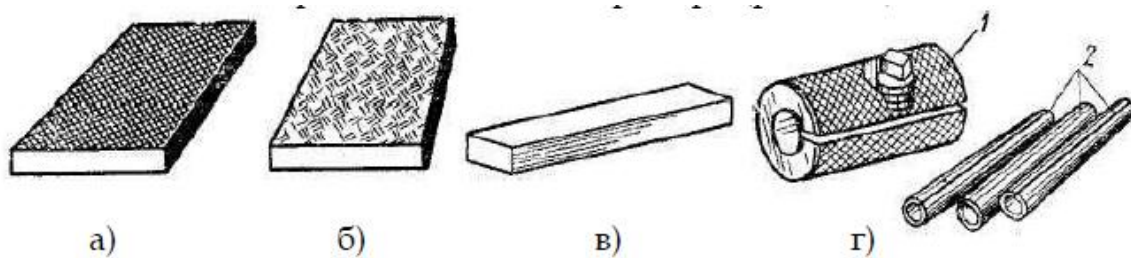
Види притирів, плоскі у вигляді плити (а, б) та бруска (в): а – для попереднього притирання; б – для чистового притирання; г - циліндричні: 1 – для притирання зовнішніх циліндричних поверхонь; 2 - для притирання внутрішніх циліндричних поверхонь
